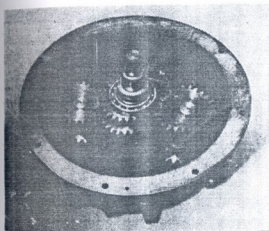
Планетарный редуктор с некруглыми колесами
